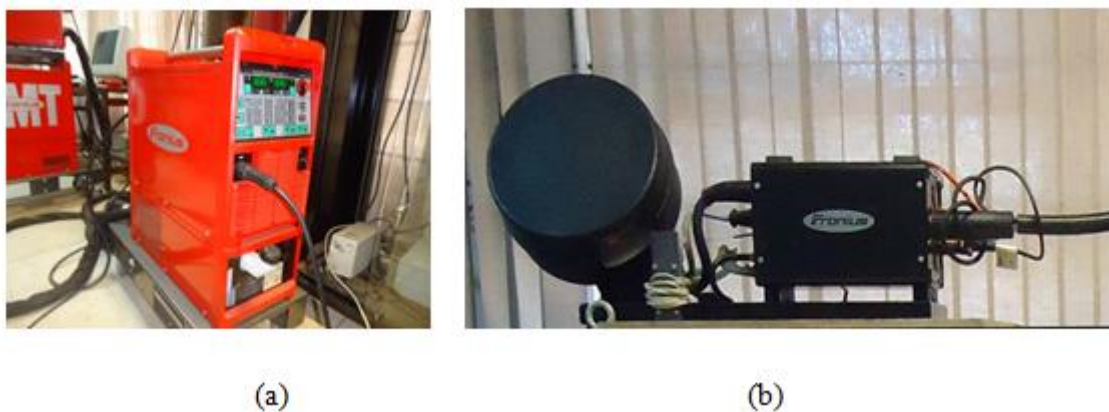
Equipamentos Fronius (a) Fonte de soldagem, (b) Alimentador de arame.
